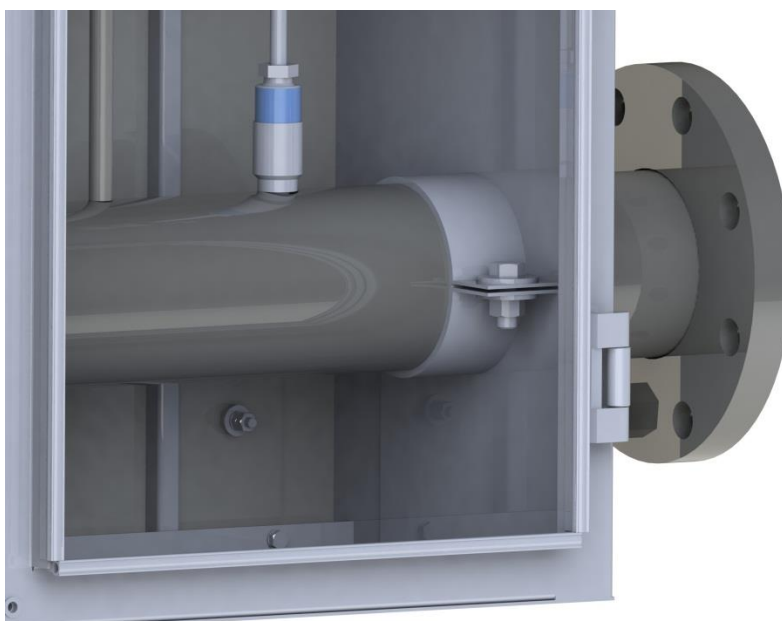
Схема фиксации шкафа на трубопроводе
